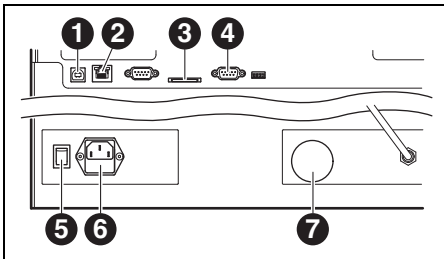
Interfaces sur la face arrière de la fraiseuse
